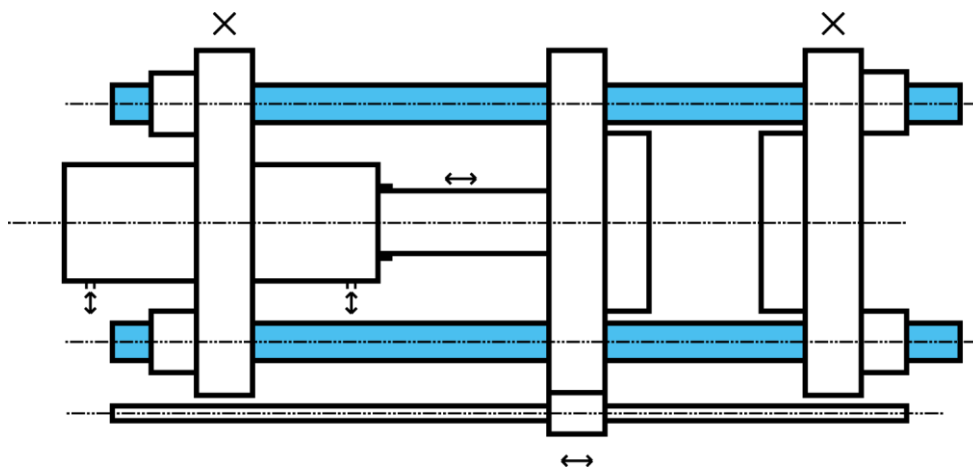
Varianta B – Uzavírací systém s hydraulickým pohonem a kloubovým mechanismem
